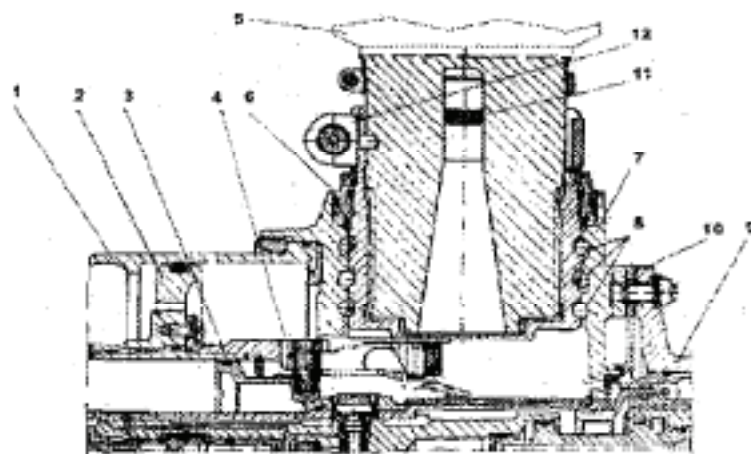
Крепление лопастей ВИШ: 1-цилиндр; 2-поршень; 3-траверса; 4-палец стакана; 5-лопасть; 6-стакан; 7-корпус втулки; 8-шарикоподшипники; 9-выходной вал редуктора; 10-торцевые шлицы; 11-балансирующий груз; 12-хомут
